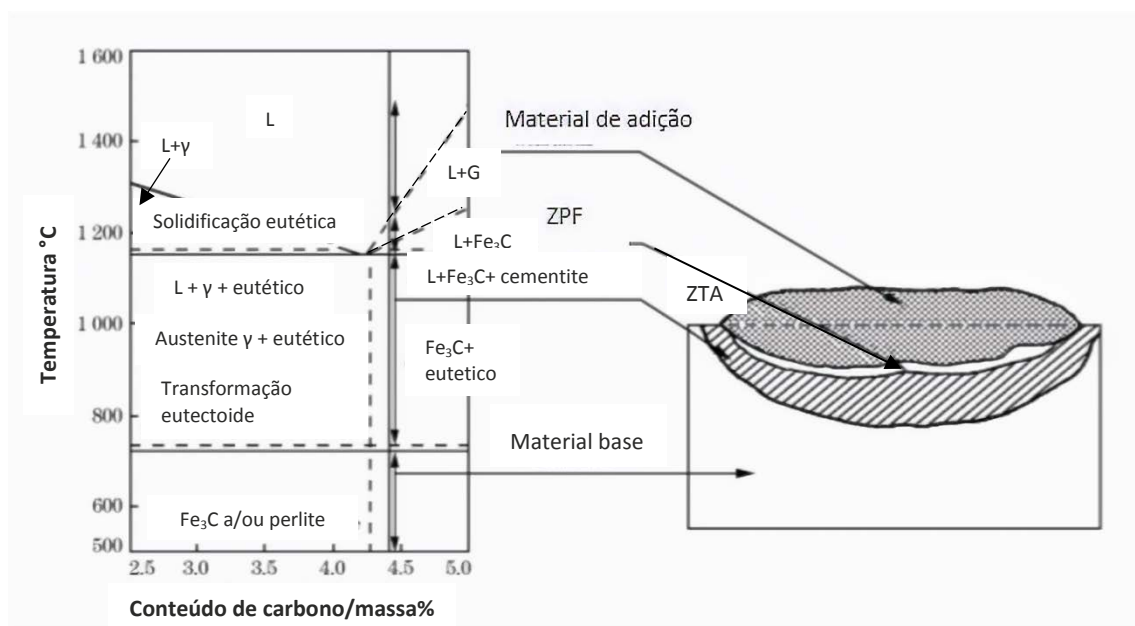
Ciclo térmico na soldadura de ferro fundido nodular [28]
